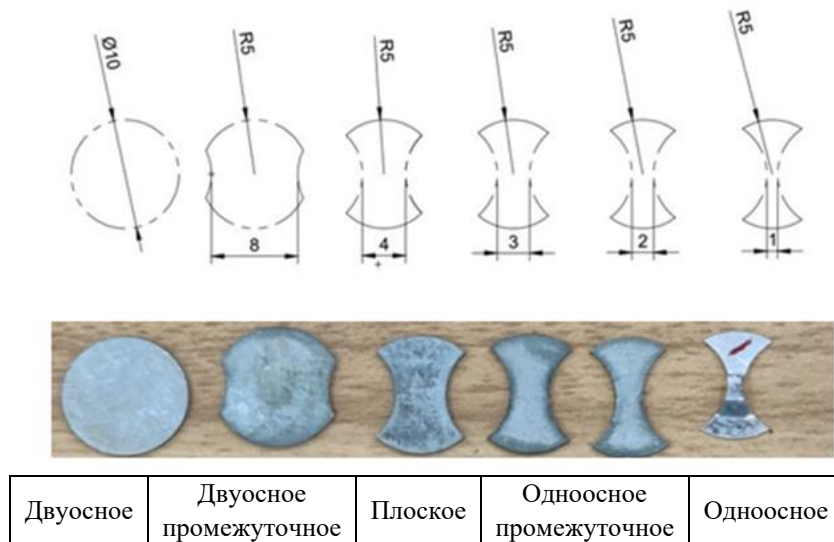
Подготовка образцов: стандарт ASTM E2218-14
